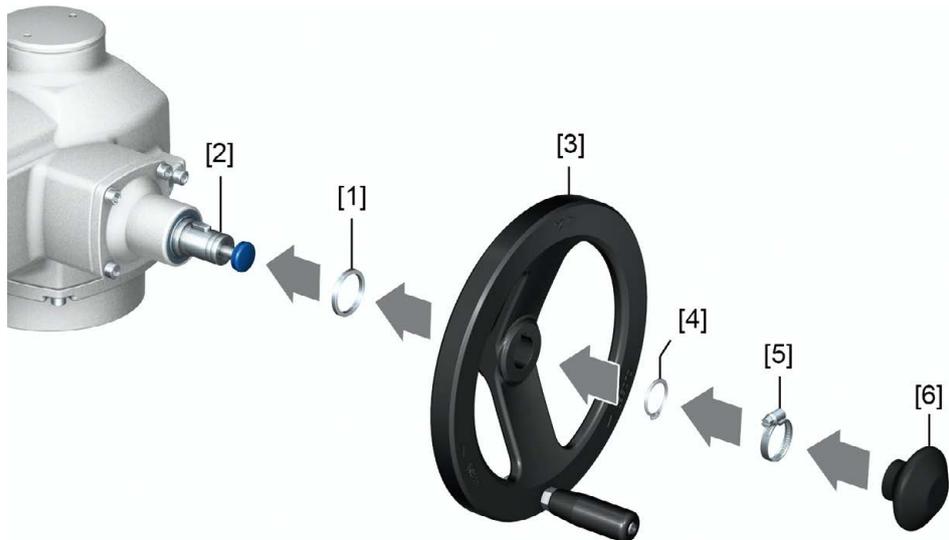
Ausführung mit dauerhaft montiertem Handrad (mit Faltenbalg)
